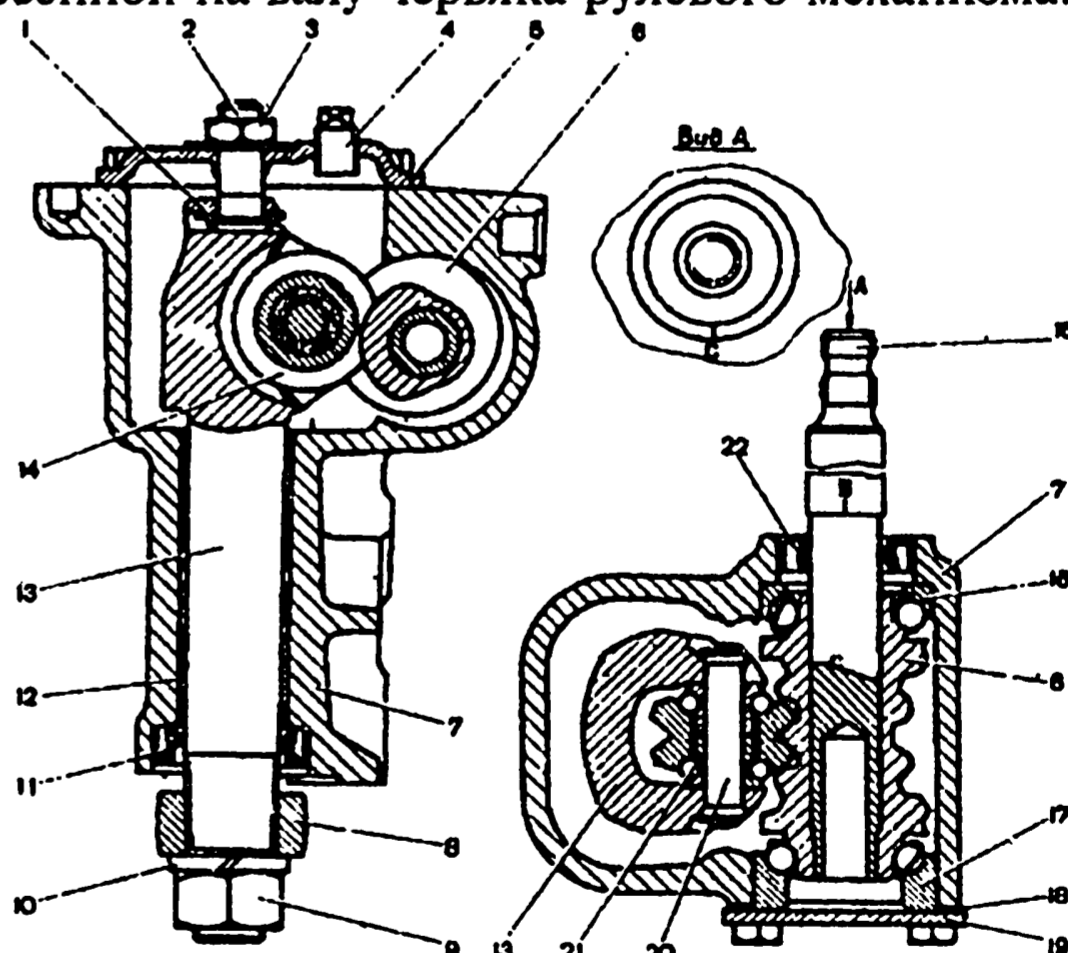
Разрез картера рулевого механизма: 1 - пластина регулировочного винта вала сошки; 2 - регулировочный винт вала сошки; 3 - гайка регулировочного винта; 4 - пробка маслоналивного отверстия; 5 - крышка картера рулевого механизма; 6 - червяк; 7 - картер рулевого механизма; 8 - сошка; 9 - гайка крепления сошки к валу; 10 - шайба пружинная гайки крепления сошки; 11 - сальник вала сошки; 12 - бронзовая втулка вала сошки; 13 - вал сошки; 14 - ролик вала сошки; 15 - вал червяка; 16 - верхний шарикоподшипник; 17 - нижний шарикоподшипник; 18 - регулировочные прокладки; 19 - нижняя крышка подшипника червяка; 20 - ось ролика; 21 - шариковый подшипник ролика; 22 - сальник вала червяка; В, С - метки
